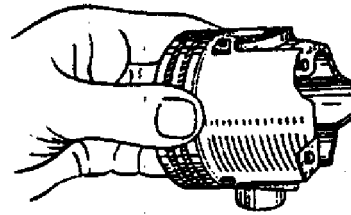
O pino não deve cair ao ser posicionado verticalmente
